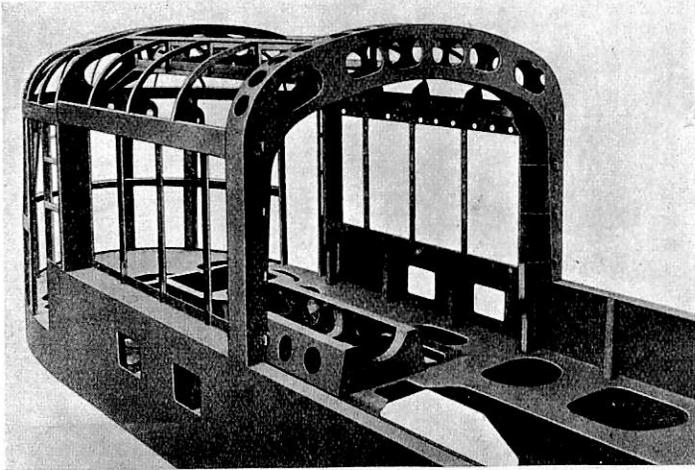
Maschinenwagen. Vorderteil mit geschweißtem Kasten-gerippe.
